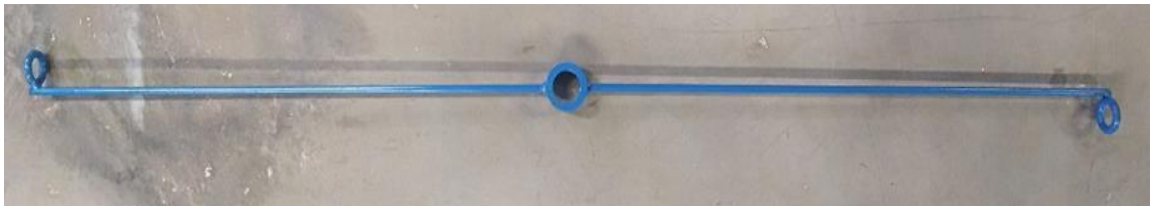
Resultado final de la fabricación de la probeta y placa de ensamble.
